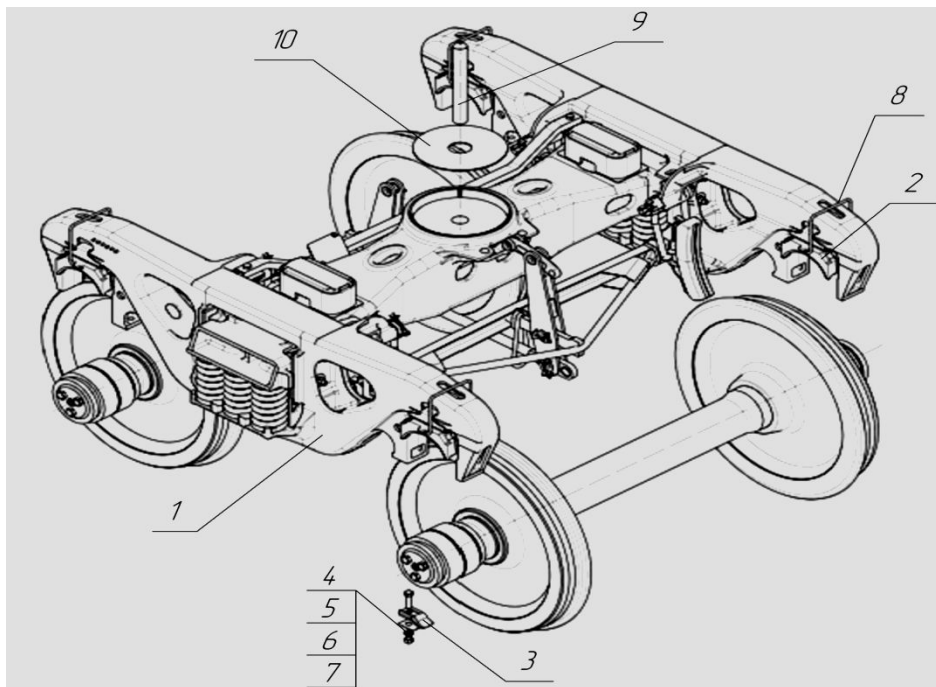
Разборка и сборка тормозной рычажной передачи
